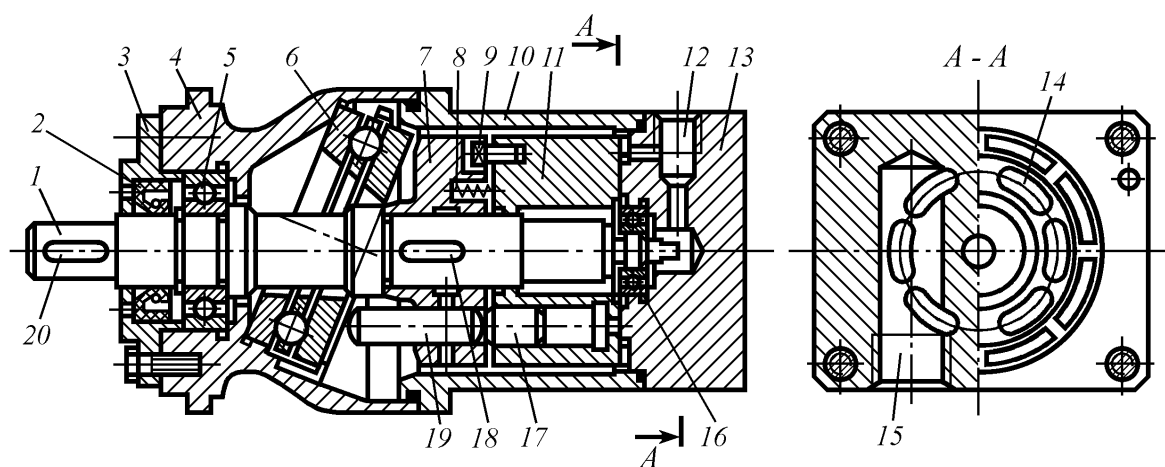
Нерегулируемый аксиально-поршневой гидромотор с неподвижным наклонным диском и вращающимся блоком цилиндров типа Г15-22Р: 1 – вал; 2 – уплотнительная манжета 3 – торцевая крышка; 4 – крышка; 5, 6, 16 – шариковые радиальные и упорный подшипники; 7, 11 – части составного блока цилиндров; 8 – пружина; 9 – штифт; 10 – корпус; 12, 15 – отверстия; 13 – задняя крышка; 14 – проходные отверстия; 17, 19 – поршни; 18, 20 – шпонки
